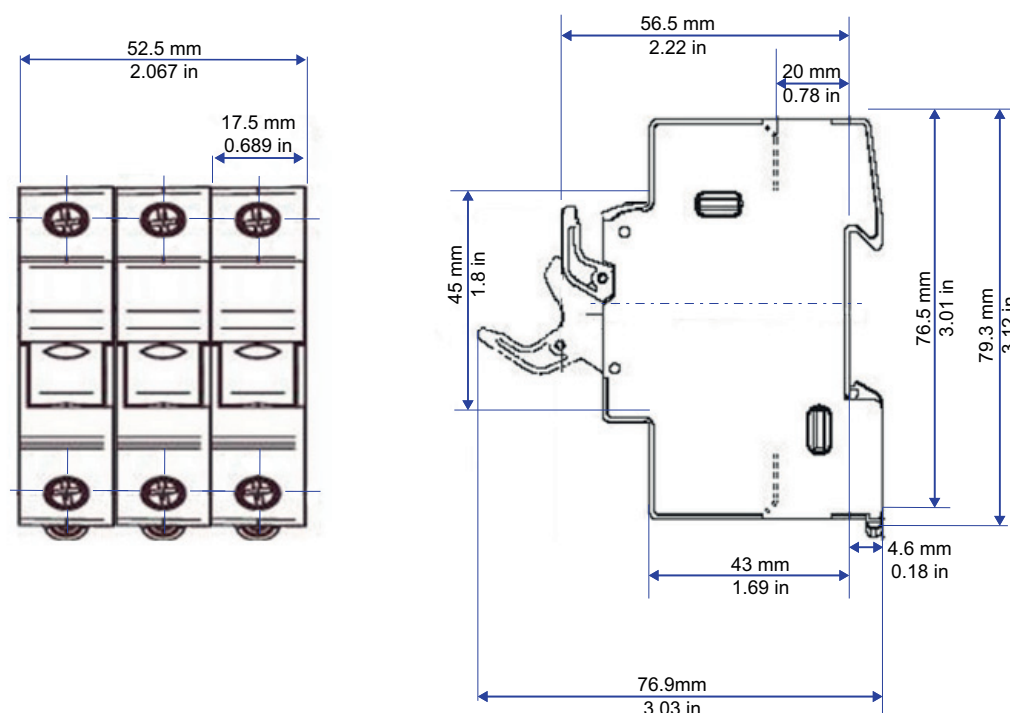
Dimensions du porte-fusible : CUS103 (10x38 mm)
